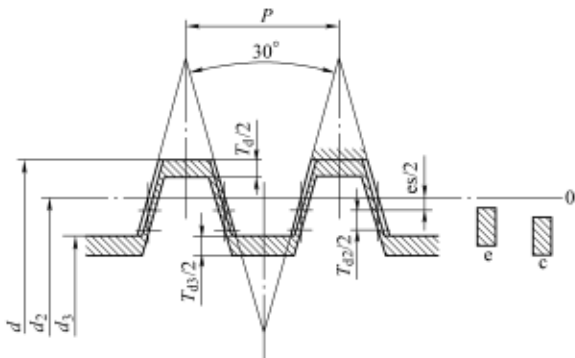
梯形螺纹外螺纹的公差带位置
